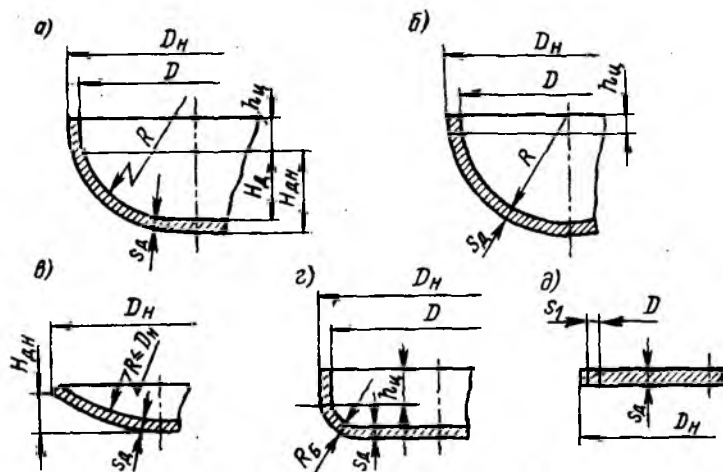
Конструкции днищ сварных аппаратов
